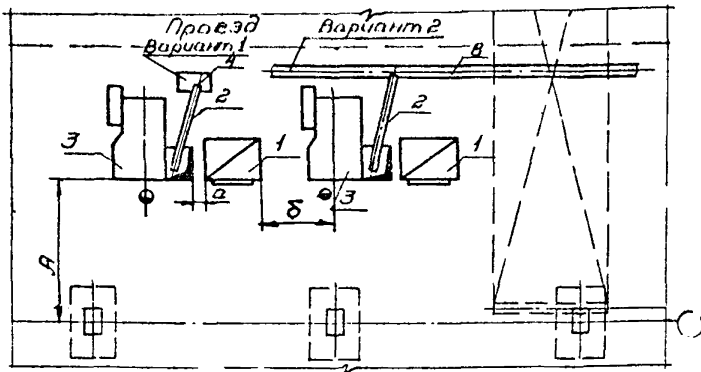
Схема расположения штамповочных линий на базе ПКМ:
